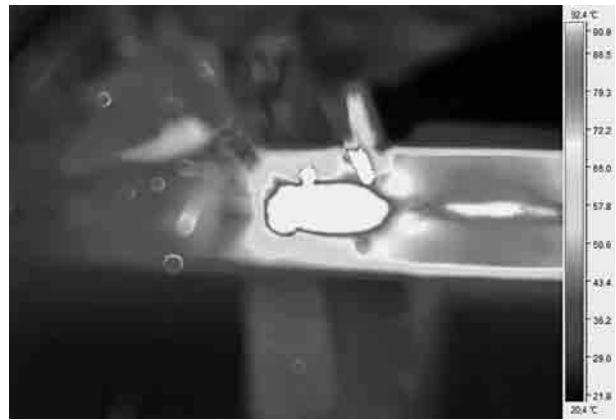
Инфракрасная съемка процесса сварки стальных деталей при газодинамическом охлаждении: 1 — свариваемые детали; 2 — сварной шов; 3 — линия нагрева и остывания зоны термического влияния; 4 — место воздействия охлаждающего газа; 5 — линия нагрева основного металла
